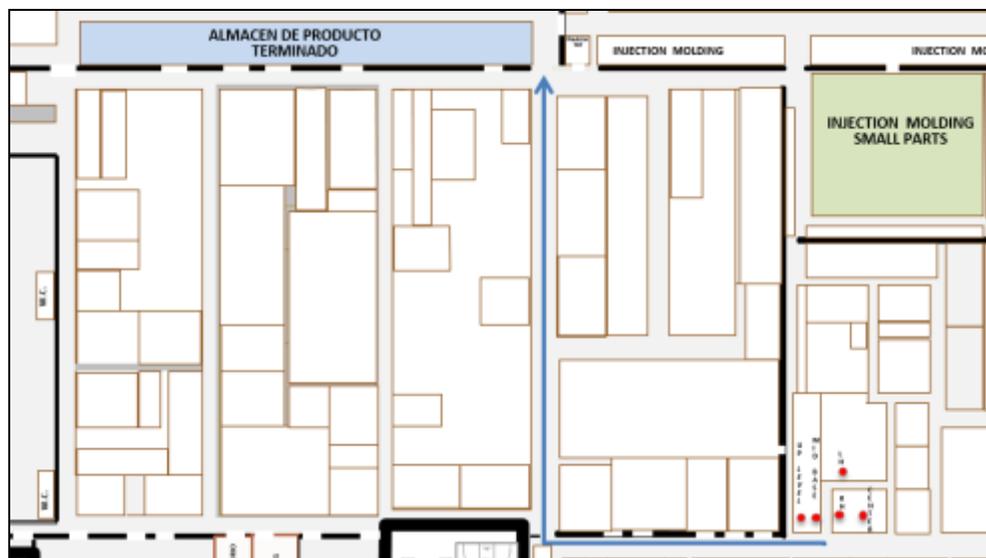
Vista de sección de Layout de recorrido de materialista externo.
